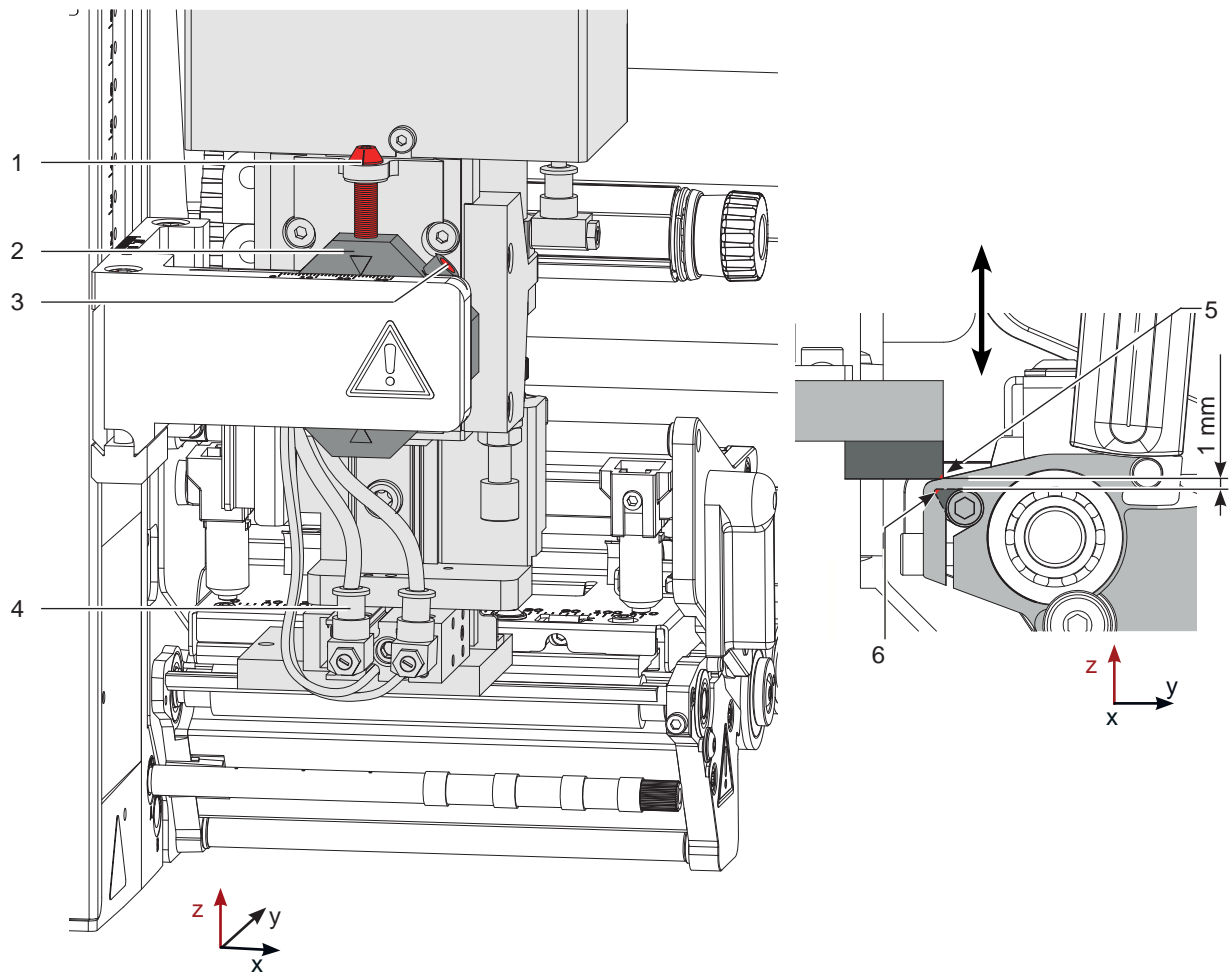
Verschiebung der Stempelbaugruppe in Z-Richtung
